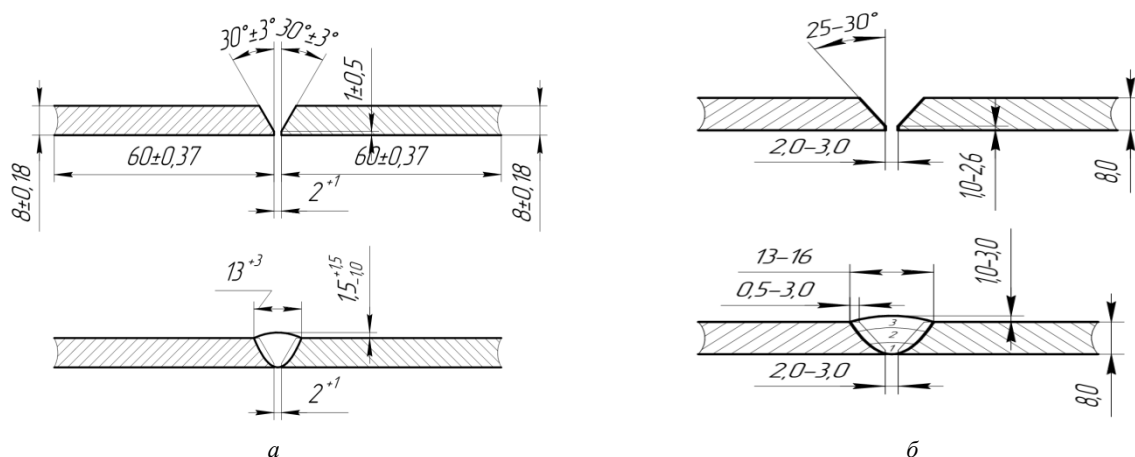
Конструктивные элементы и размеры сварного соединения: а – С17 (ГОСТ 16037-80, выполненного методом РДС) полученные с использованием шаблона; б – труба $\varnothing 219 \times 8$ мм с разделкой кромок по форме Тр-1, выполненного методом РДС (СТО Газпром 15-1.1-002-2023)
